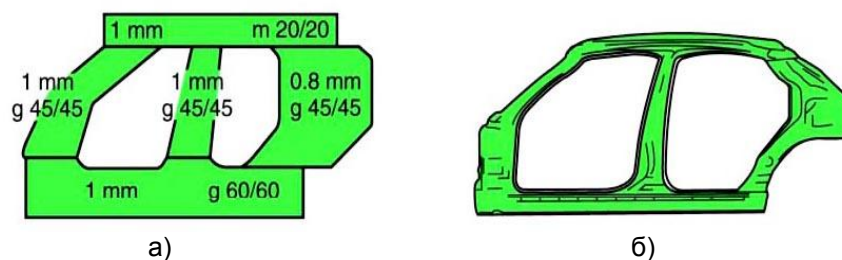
Составная заготовка боковины автомобиля (а) и штампованная деталь (б)
